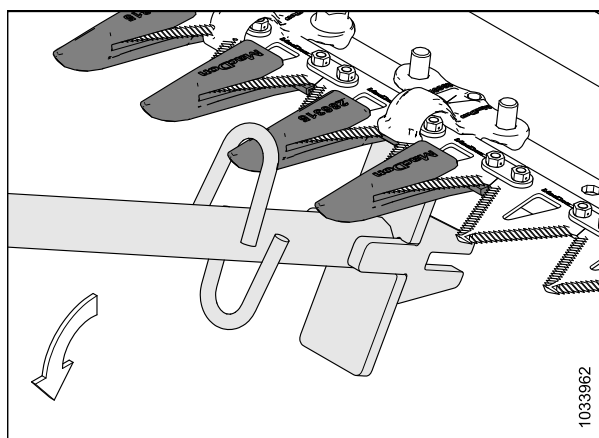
Регулировка смещением вниз — заостренный противорезающий палец
